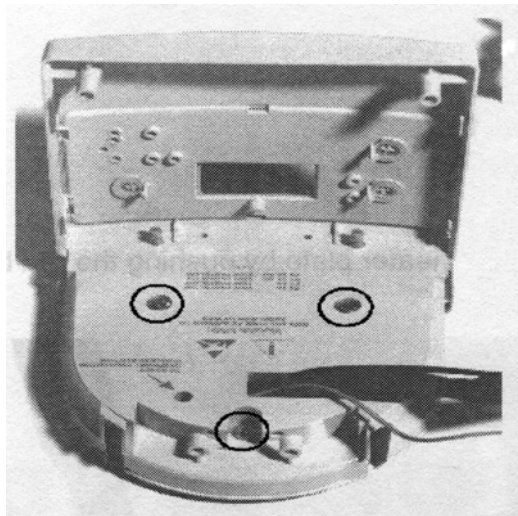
Platzierung der Heizplattenschrauben
